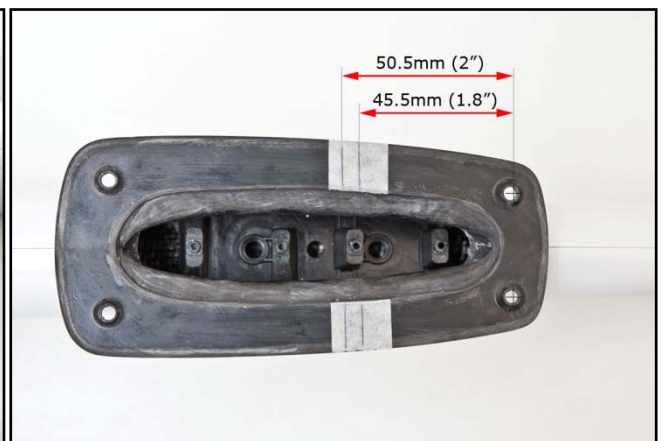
Подготовка фюзеляжа для установки платформы машинок
